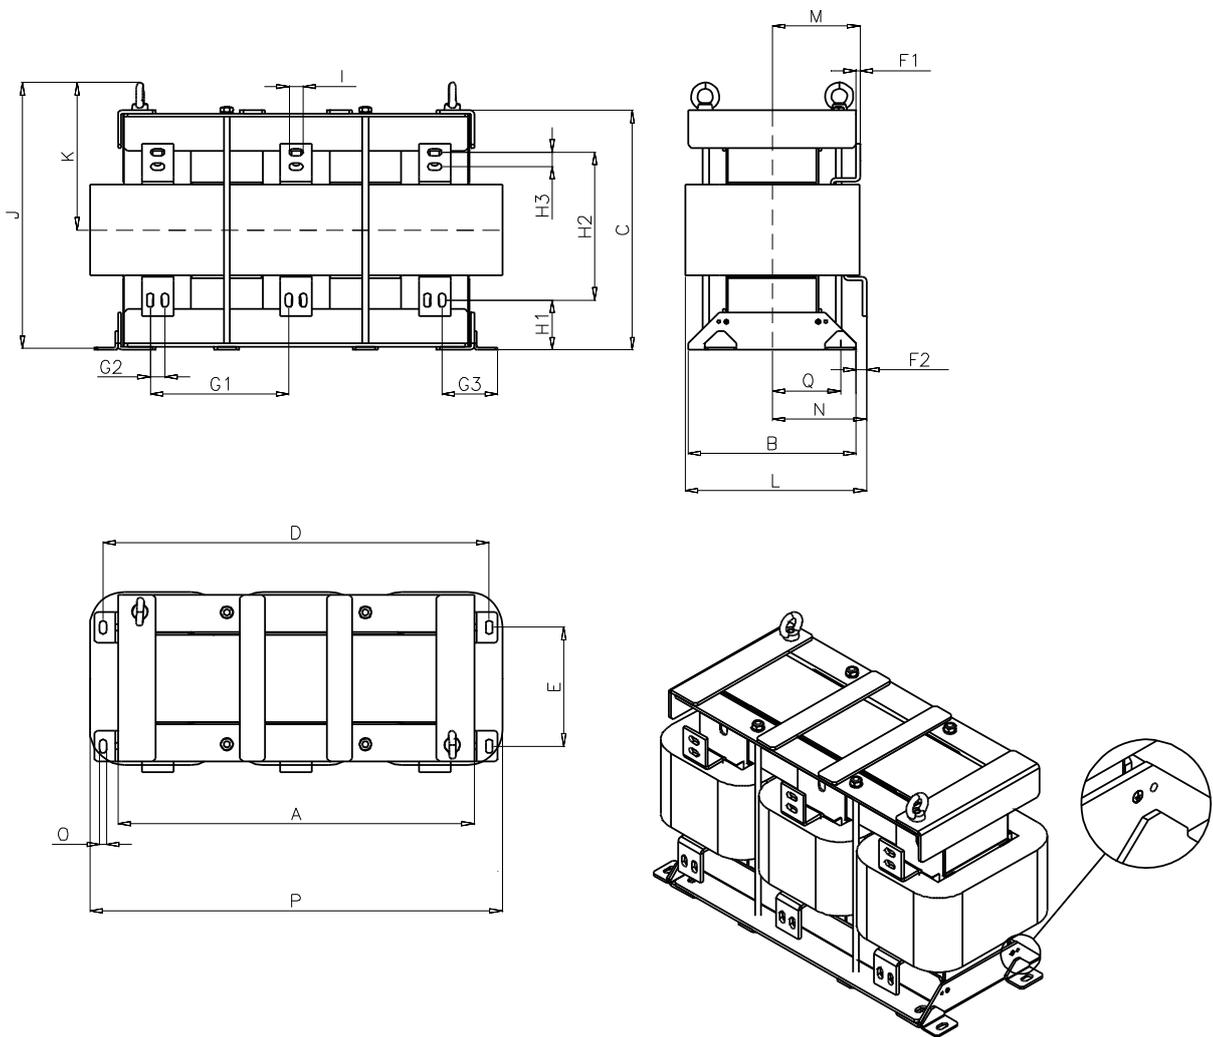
Disegno quotato bobina di rete 6SL3000-0EH41-4AA0
